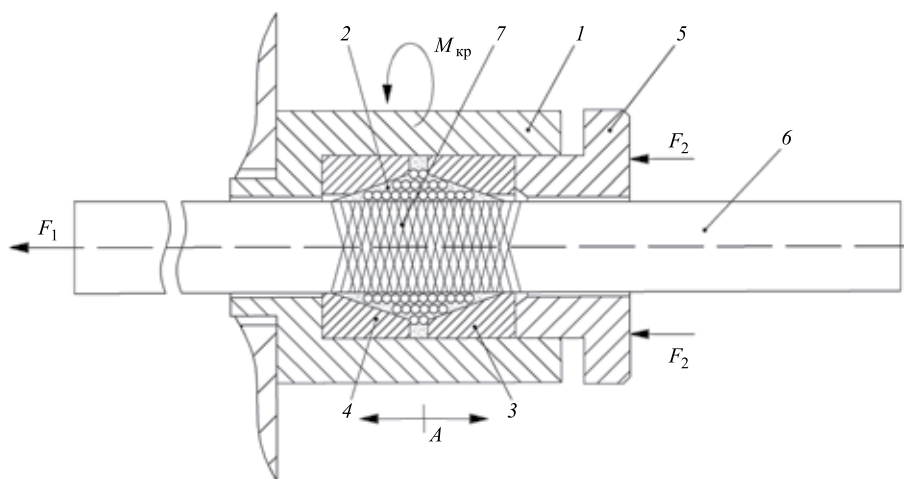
Конструкция охватывающего инструмента для регуляризации микрогеометрии поверхности обрабатываемой заготовки
